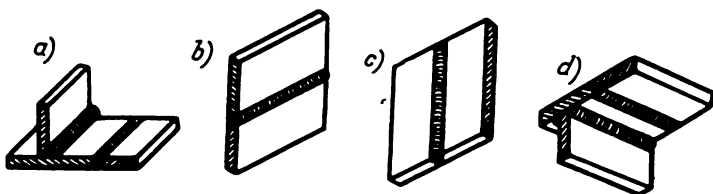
Types de soudures suivant leur position dans l'espace
